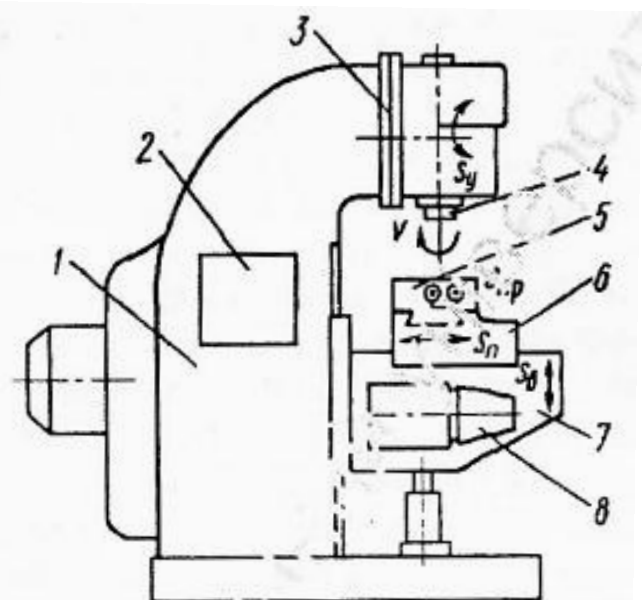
Вертикально-фрезерувальний верстат
